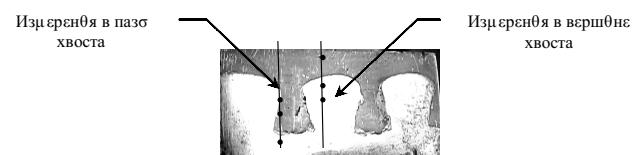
Биметаллический переходник с границей сварного соединения типа «ласточкин хвост»
